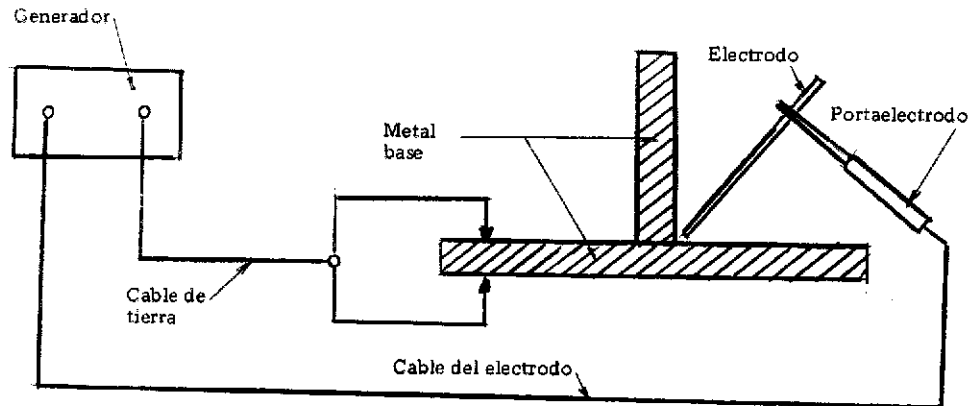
Esquema del proceso de soldadura de arco.
